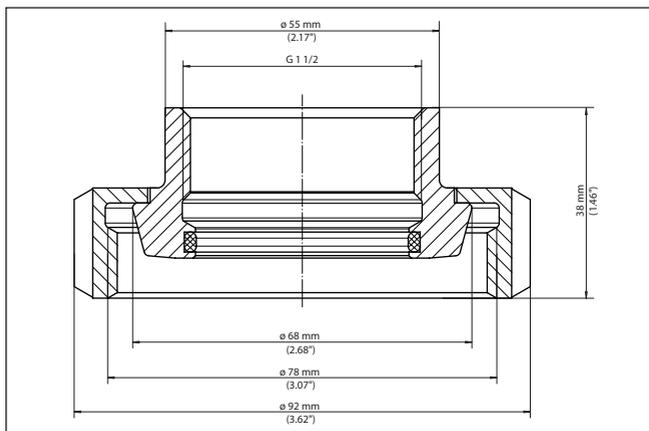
Dimensiones adaptador de rosca G1½ (DIN 3852-X) a racor roscado DN 50 (DIN 11851) PN 16
